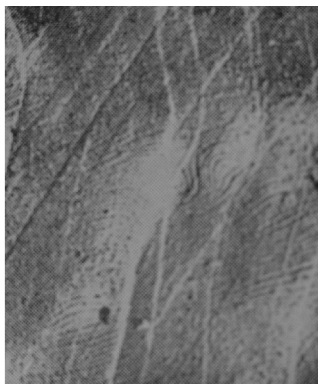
焊缝凝固裂纹的断口形貌
